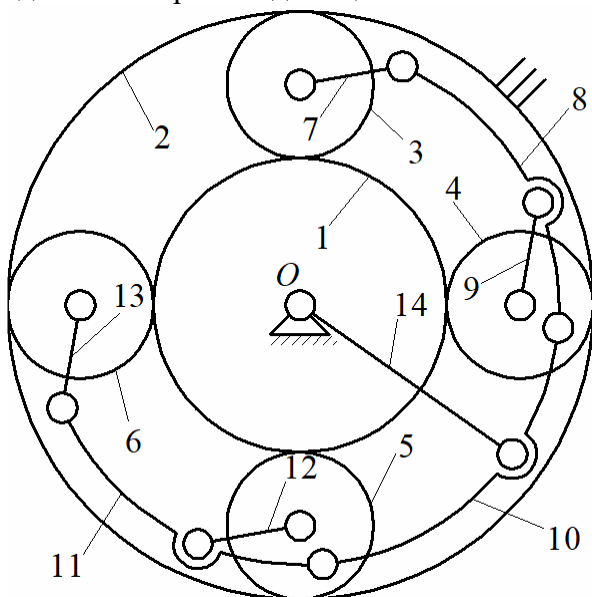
Планетарный механизм с четырьмя безводильными сателлитами
